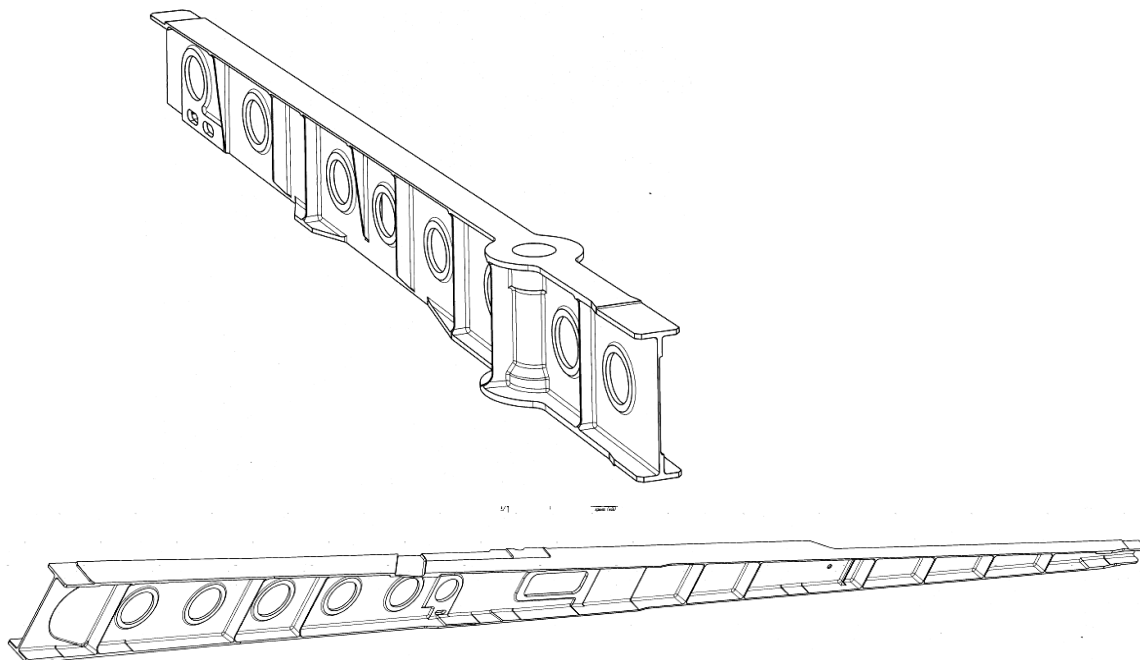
Типовые конструкции детали ”Лонжерон”
